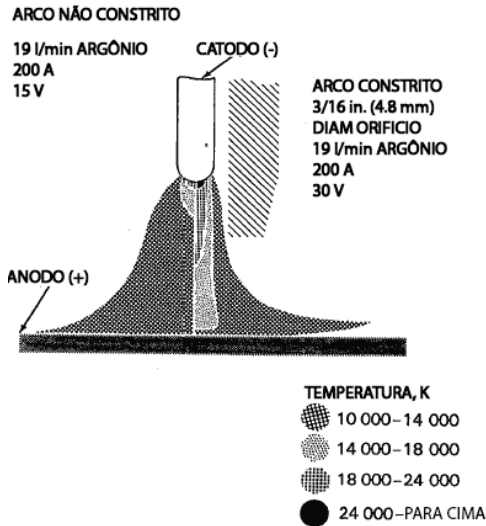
Comparação Plasma-TIG sob as mesmas condições de soldagem.
